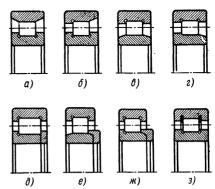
Роликоподшипники с короткими цилиндрическими роликами ролиорялные, ГОСТ 8328—57; а радиальные тов на наружном кольце, тип 2000; δ — с однобортовым наружным кольцом, тип 12000; ϵ — без бортов на внутреннем кольце, тип 32000; г— с однобортовым внутренним кольцом, тип 42000; ∂ — то же и с плоским упорным кольцом, тип 92000; - без бортов на внутреннем кольце и с фасонным упорным кольцом, тип 52000: ж - с однобортовым внутренним кольцом и с фасонным упорным кольцом, тип 62000; - неразъемный, с двумя запорными шайбами, тип 102000
